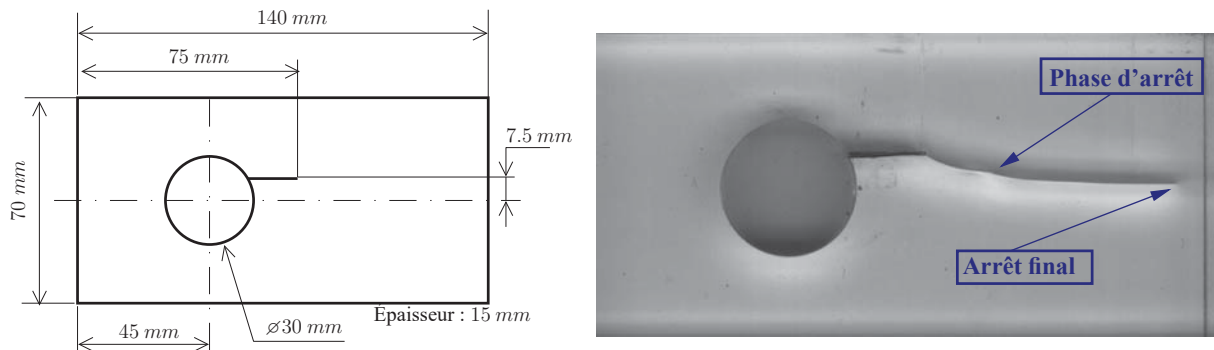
Géométrie des éprouvettes testées et éprouvette post mortem
